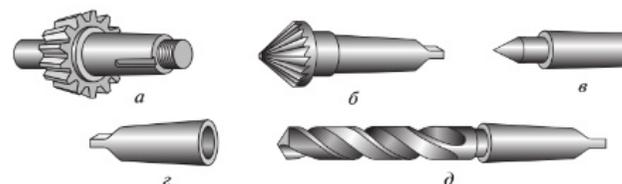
Типовые детали с коническими поверхностями: а — коническое зубчатое колесо; б — коническая зенковка; в — центр токарного станка; з — переходная втулка; д — сверло с коническим хвостовиком
